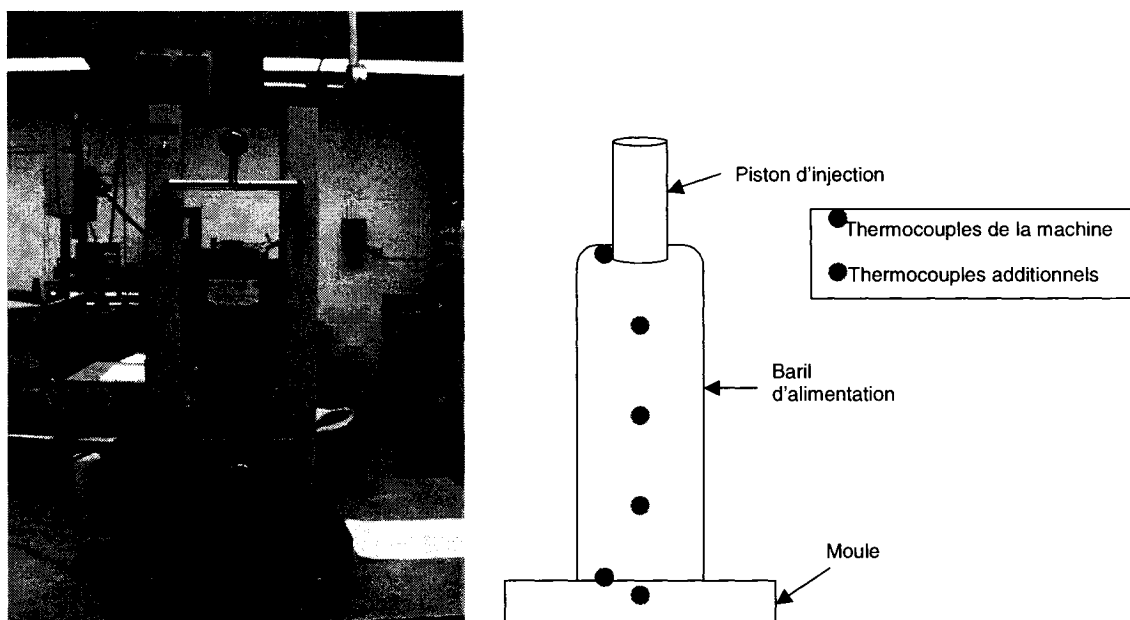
Machine de moulage Ray-ran et l'emplacement des thermocouples
